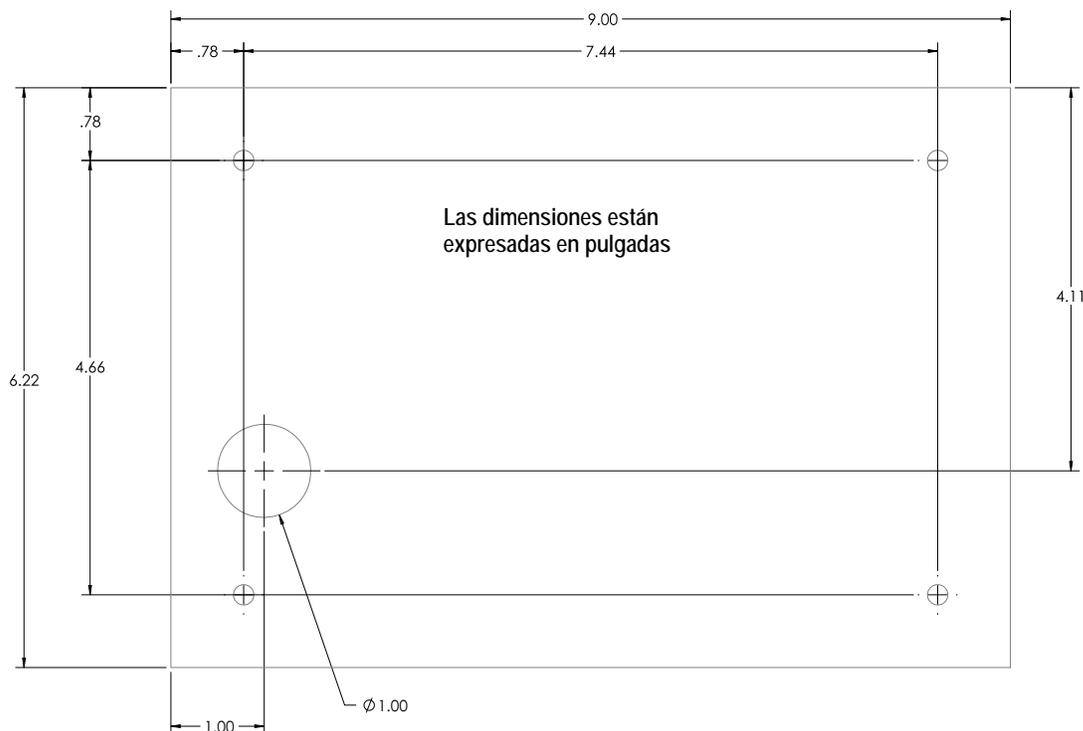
Dimensiones del montaje en panel de 7 pulgadas solo táctil
